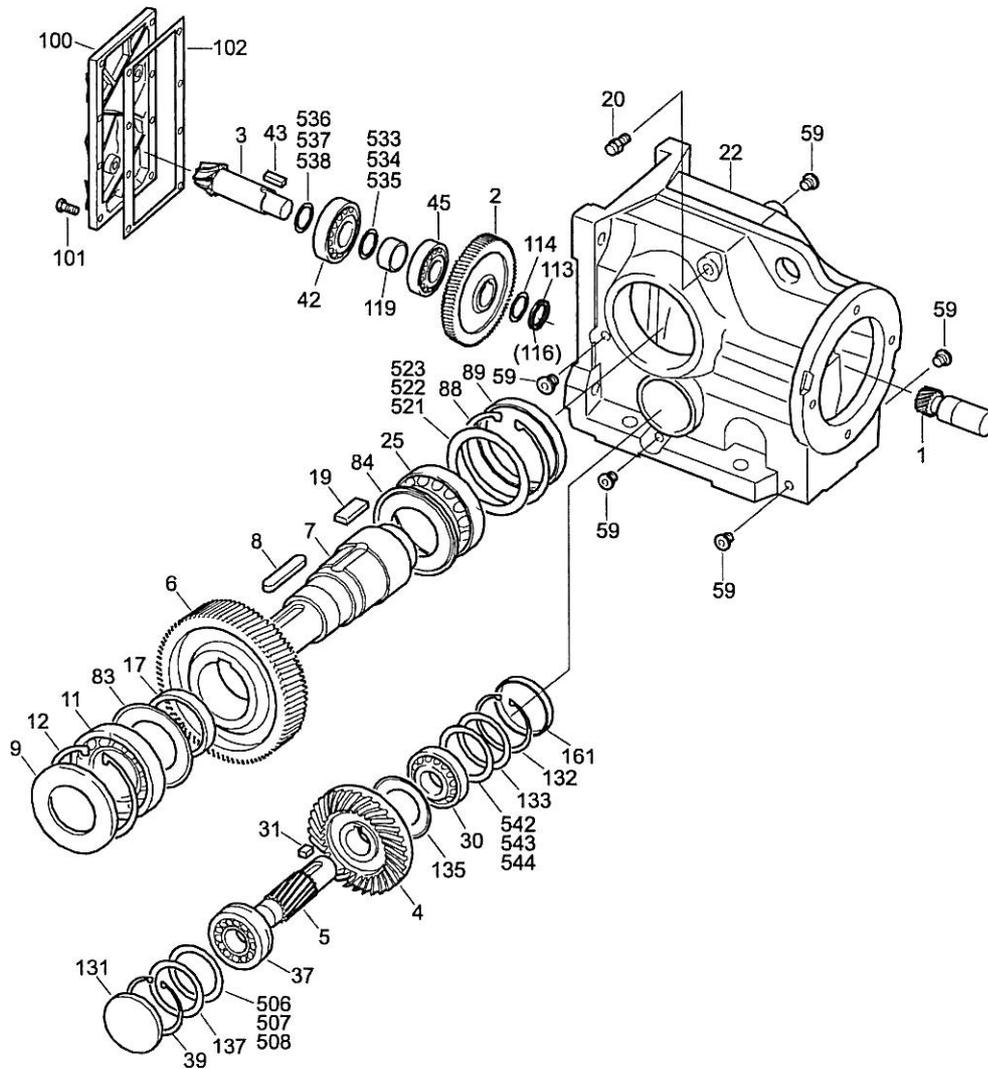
Prinzipieller Aufbau Kegelradgetriebe
